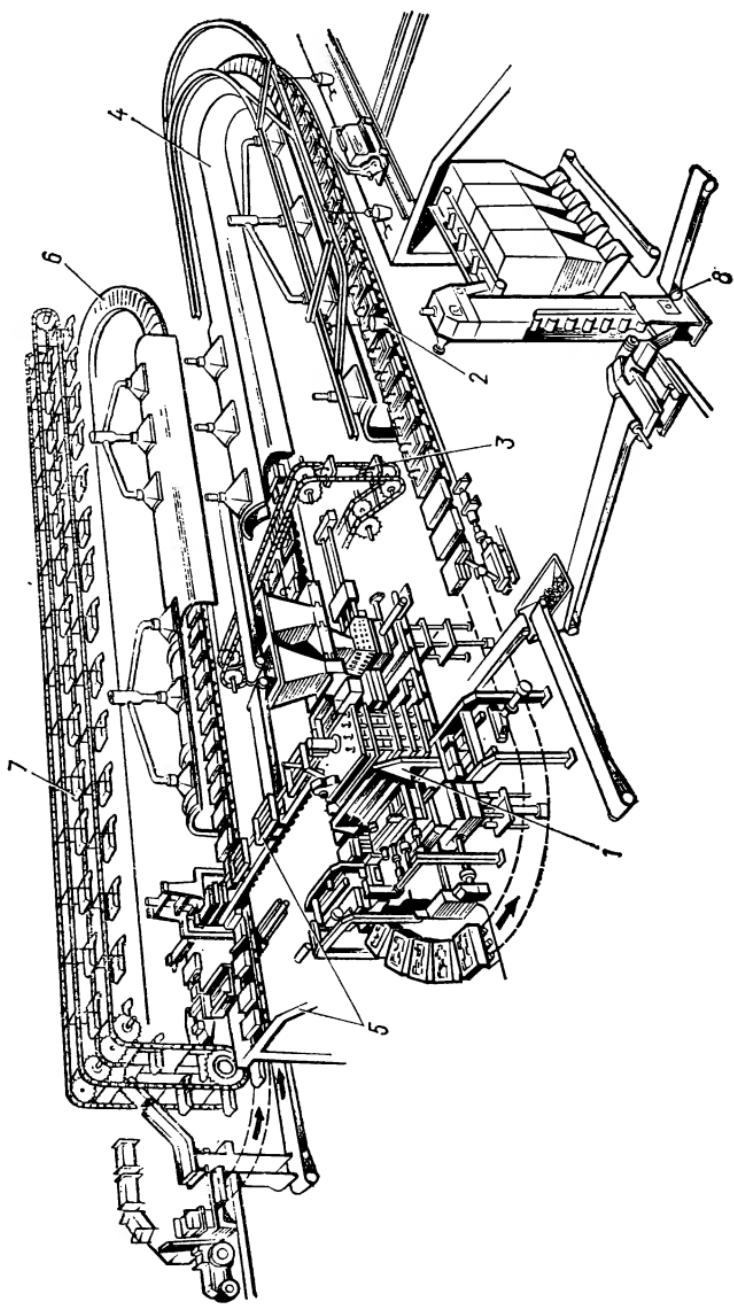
Комплексная автоматическая линия формовки — заливки-выбивки:
